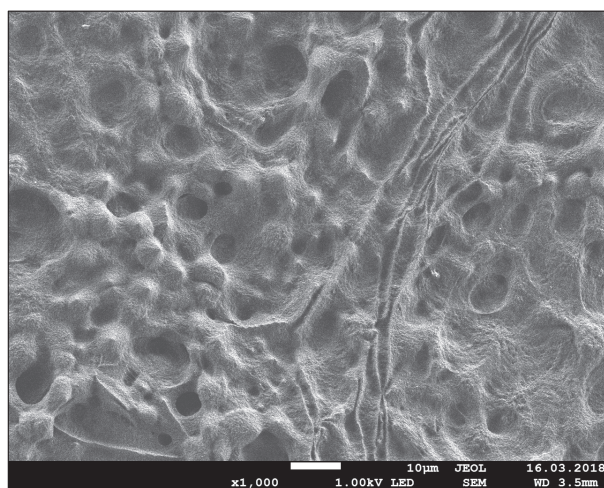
Структура материала зоны термического влияния сварного соединения при температуре сварки окружающего воздуха 1 °С.
